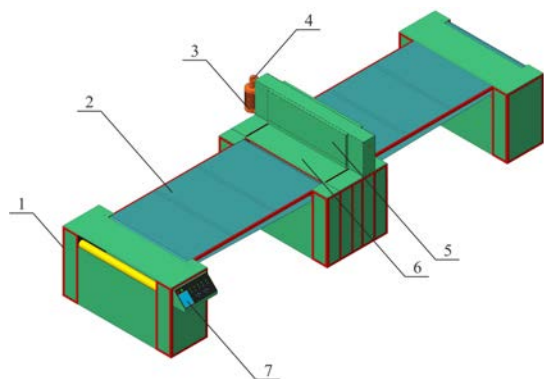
3D-модель конструкції різального верстата для автоматизованої конвеєрної лінії (вид праворуч, зі стрічкою): 1 – каркас консолі № 1; 2 – рухома стрічка; 3 – виконавчий електродвигун; 4 – редукторний механізм; 5 – захисний кожух механізму різання; 6 – робоча поверхня різального верстату; 7 – панель керування
